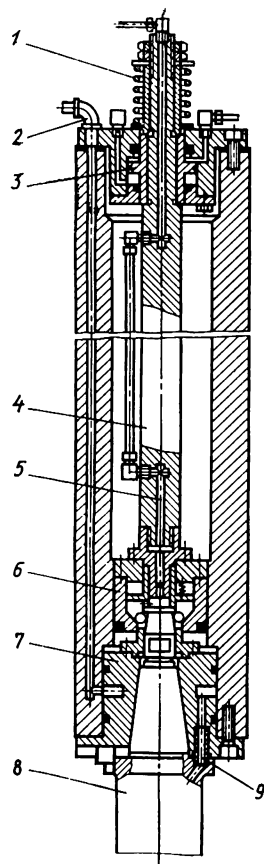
Механизм автоматического крепления резцедержателей с коническими хвостовиками станков фирмы Webster — Bennett
